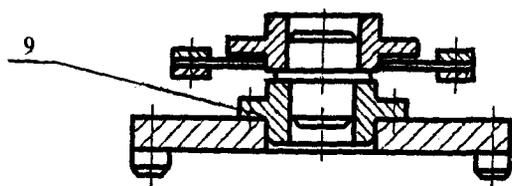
Приспособление для контроля точных цилиндрических поверхностей:
